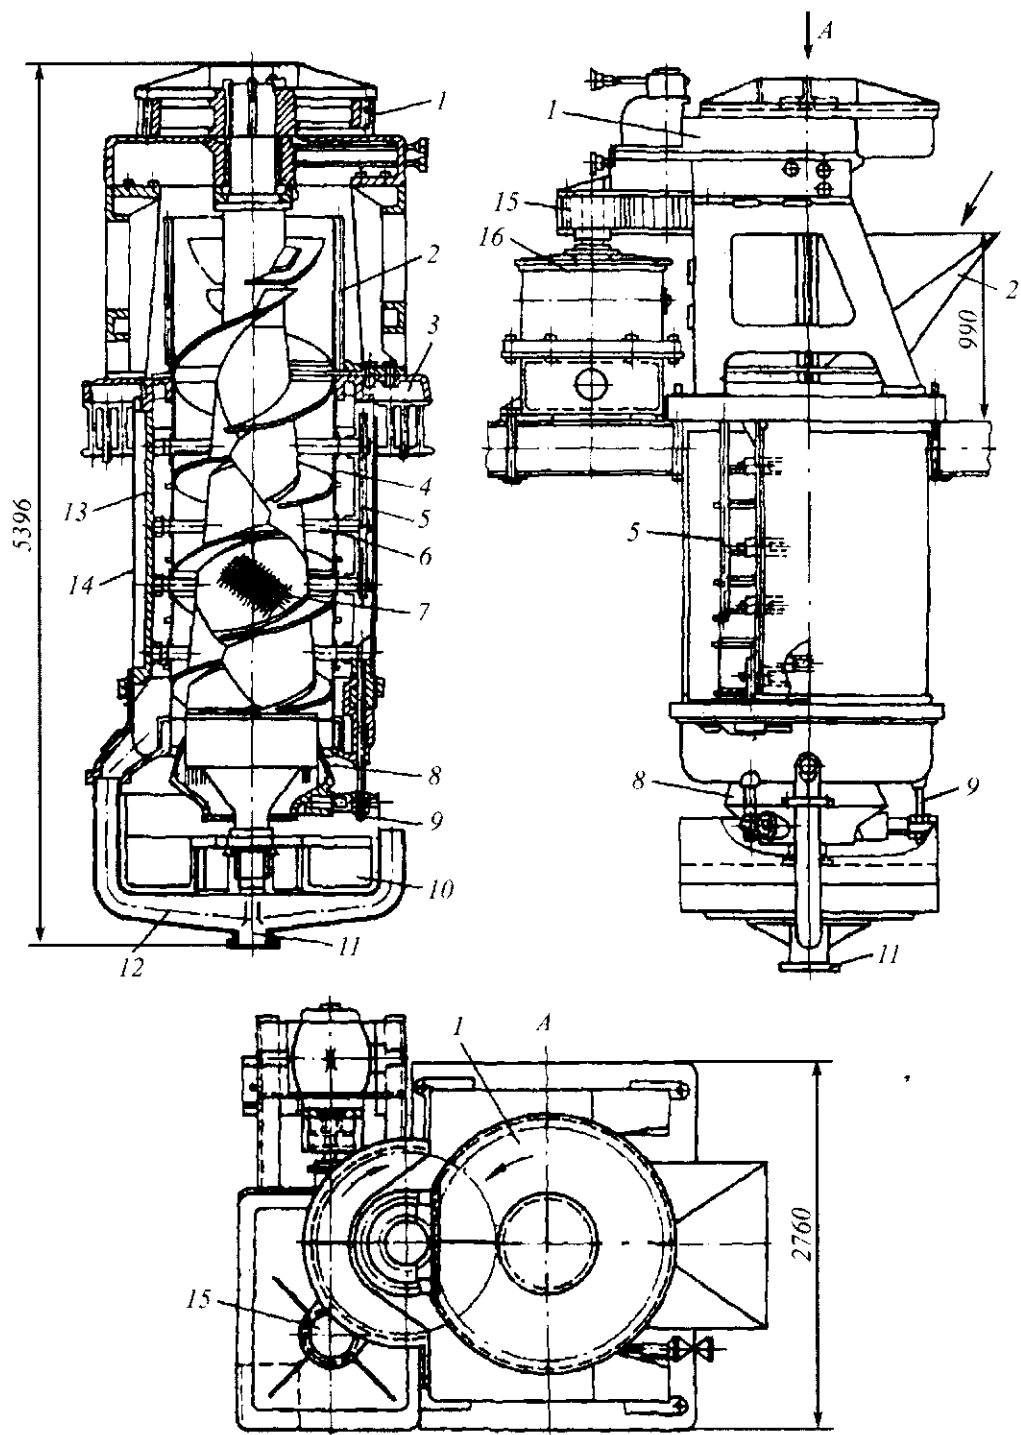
Вертикальный шнековый пресс типа ПВЖ-60
